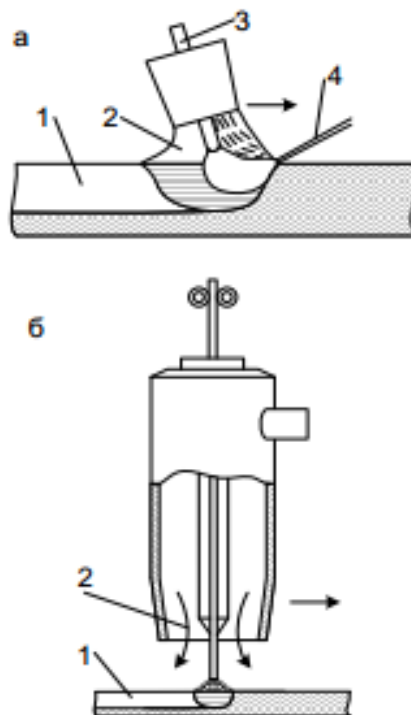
Схеми дугового зварювання в захисному газі:
